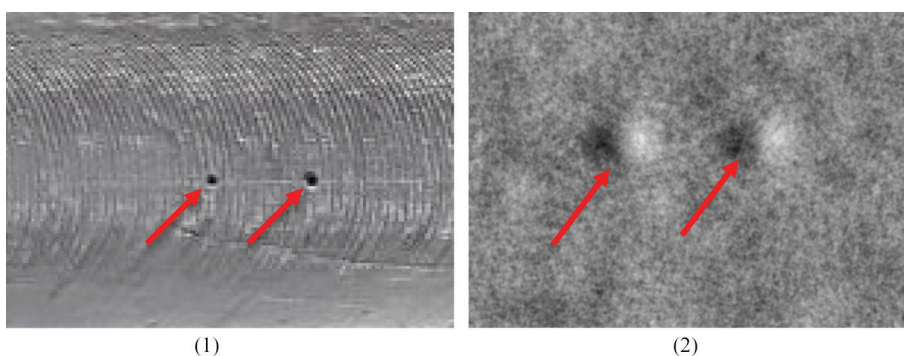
Ширографічний контроль досліджуваної ділянки зварного шва алюмінієвого зразка: загальний вигляд ділянки з дефектом (1) і типова картина виявлених дефектів (2)
